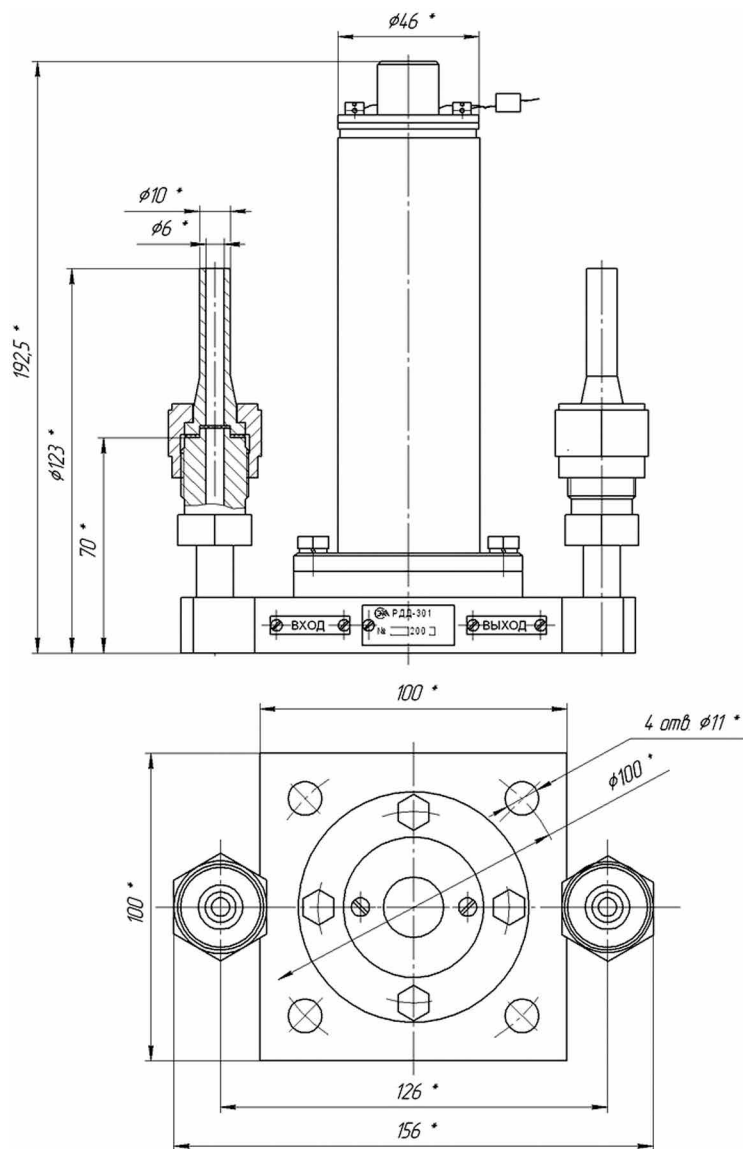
Габаритные и установочные размеры регулятора РДД-301
